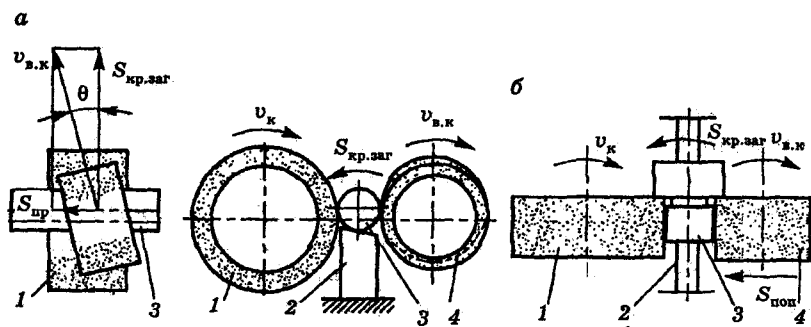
Схемы обработки на бесцентрово-шлифовальных станках: а — наружных поверхностей; б — ступенчатой формы
